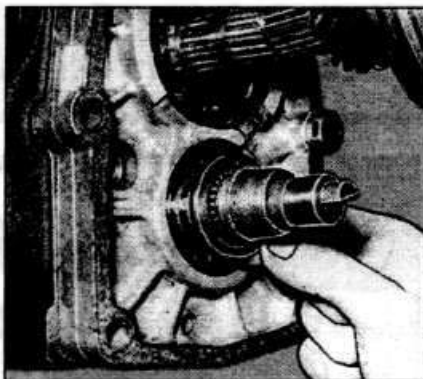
Установка дистанционной шайбы на шестерню V передачи промежуточного вала
